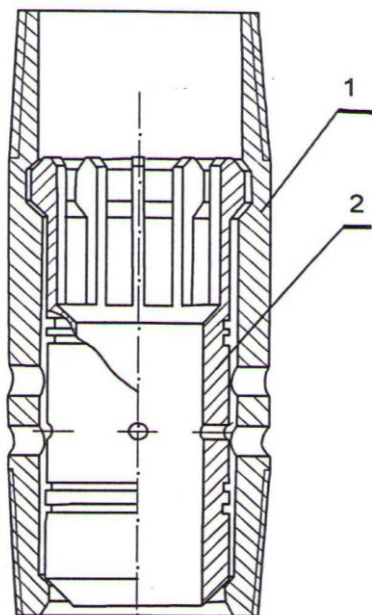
Перфорированный патрубок с забойным штуцером: 1 - перфорированный патрубок; 2 - забойный штуцер
